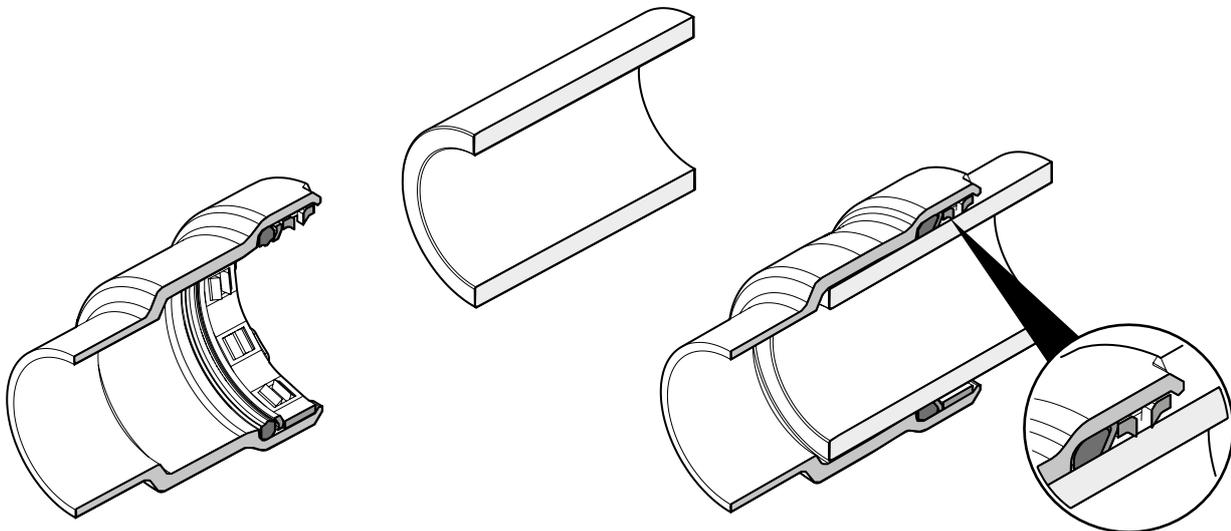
Assemblage Optifitt-Press (ouvert/serti)
